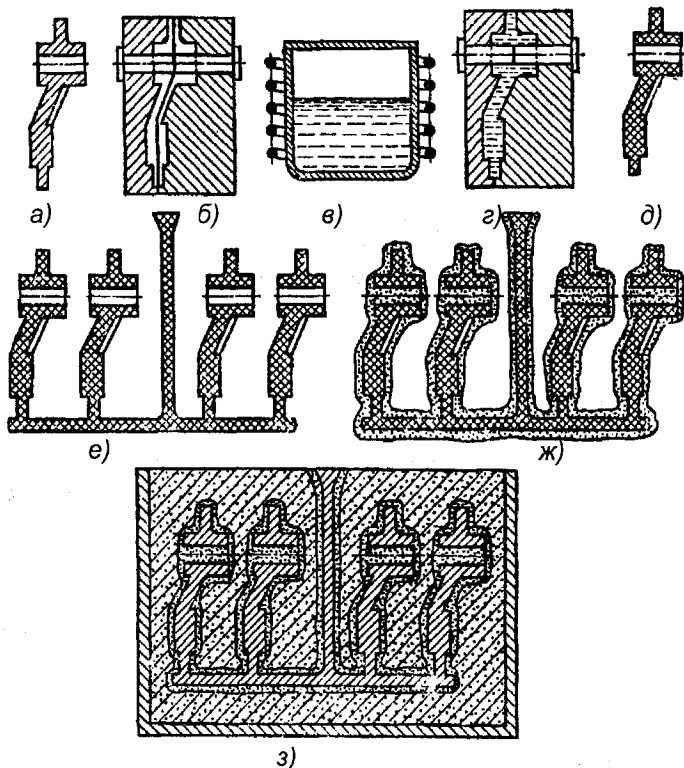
Послідовність виготовлення виливків литтям за виплавними моделями: а - виливок; б - прес-форма; в - електропіч для розплаву легкоплавкого сплаву; г - прес-форма, заповнена легкоплавким сплавом; д - легкоплавка модель; е - легкоплавкі моделі з ливниковою системою; ж - легкоплавкі моделі з нанесеним шаром вогнетривкого матеріалу; з - заформовані легкоплавкі моделі
